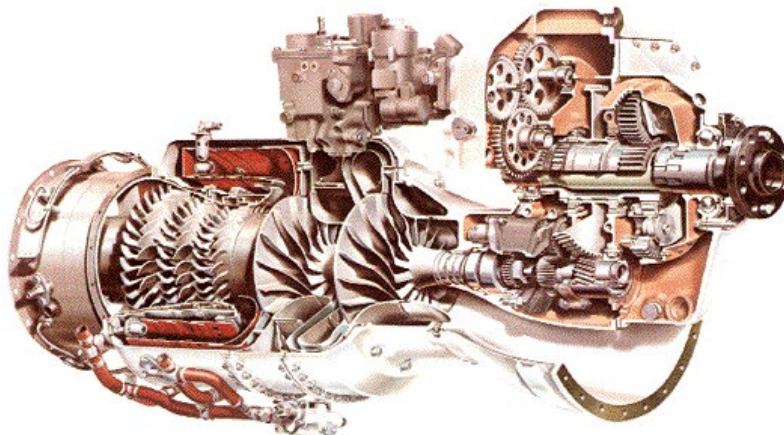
Турбовинтовой двигатель Garrett TPE331 с двухступенчатым центробежным компрессором
